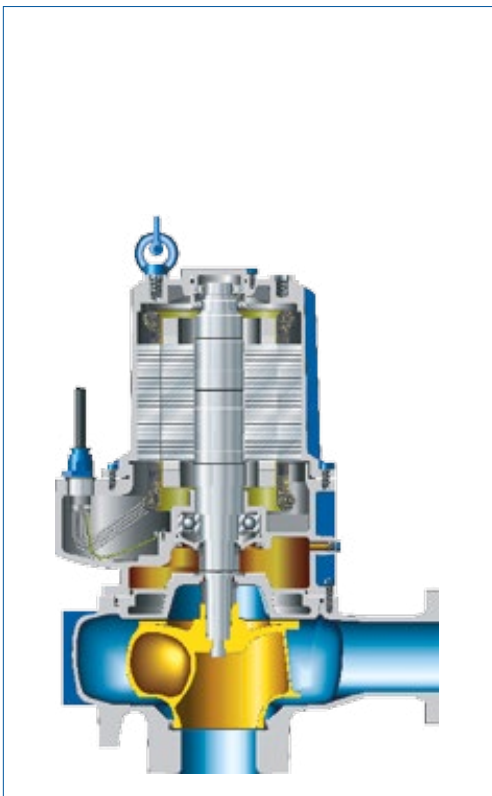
Plan en coupe d'une KRT 4 à 60 kW
